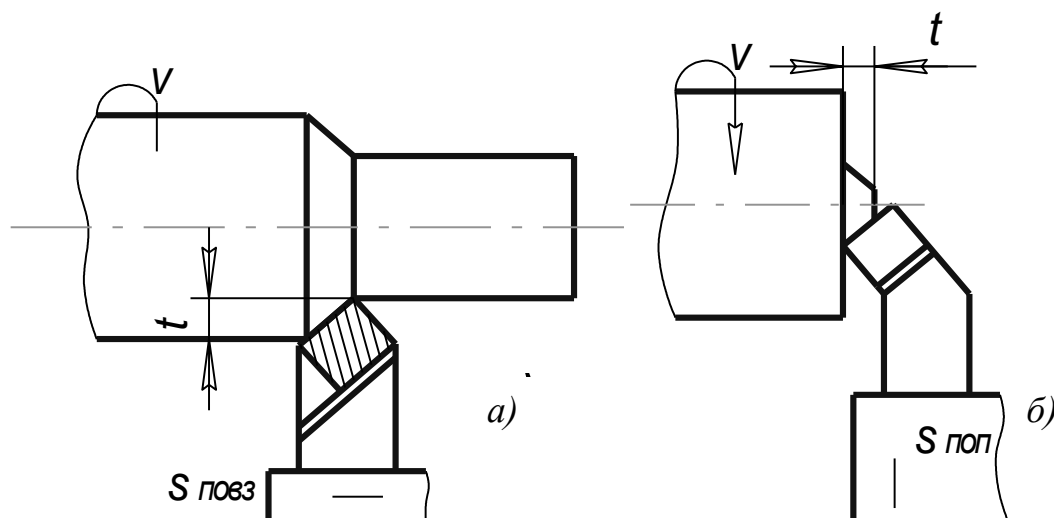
Схеми робочих рухів за токарної обробки:
